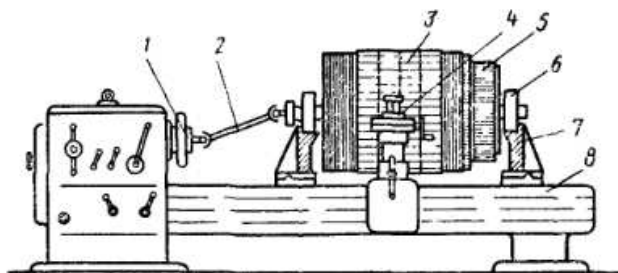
Якорь, установленный для проточки коллектора на токарно-винторезном станке
